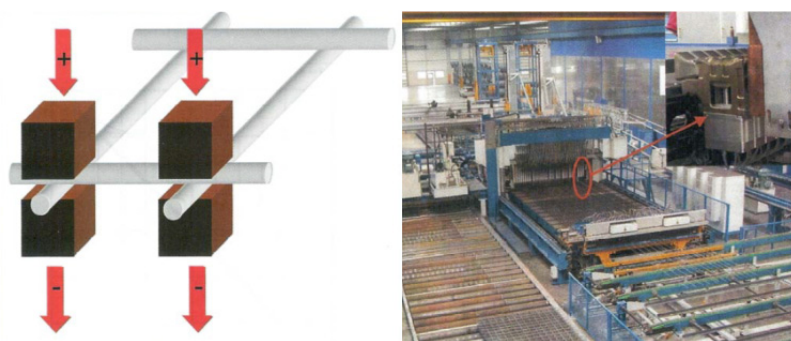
Exemplo de equipamento de soldadura directa por pontos múltiplos [16]
